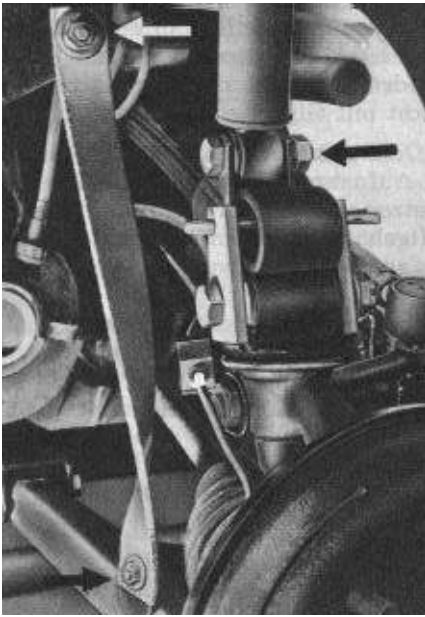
Stoßdämpfer- und Fangbandbefestigung
